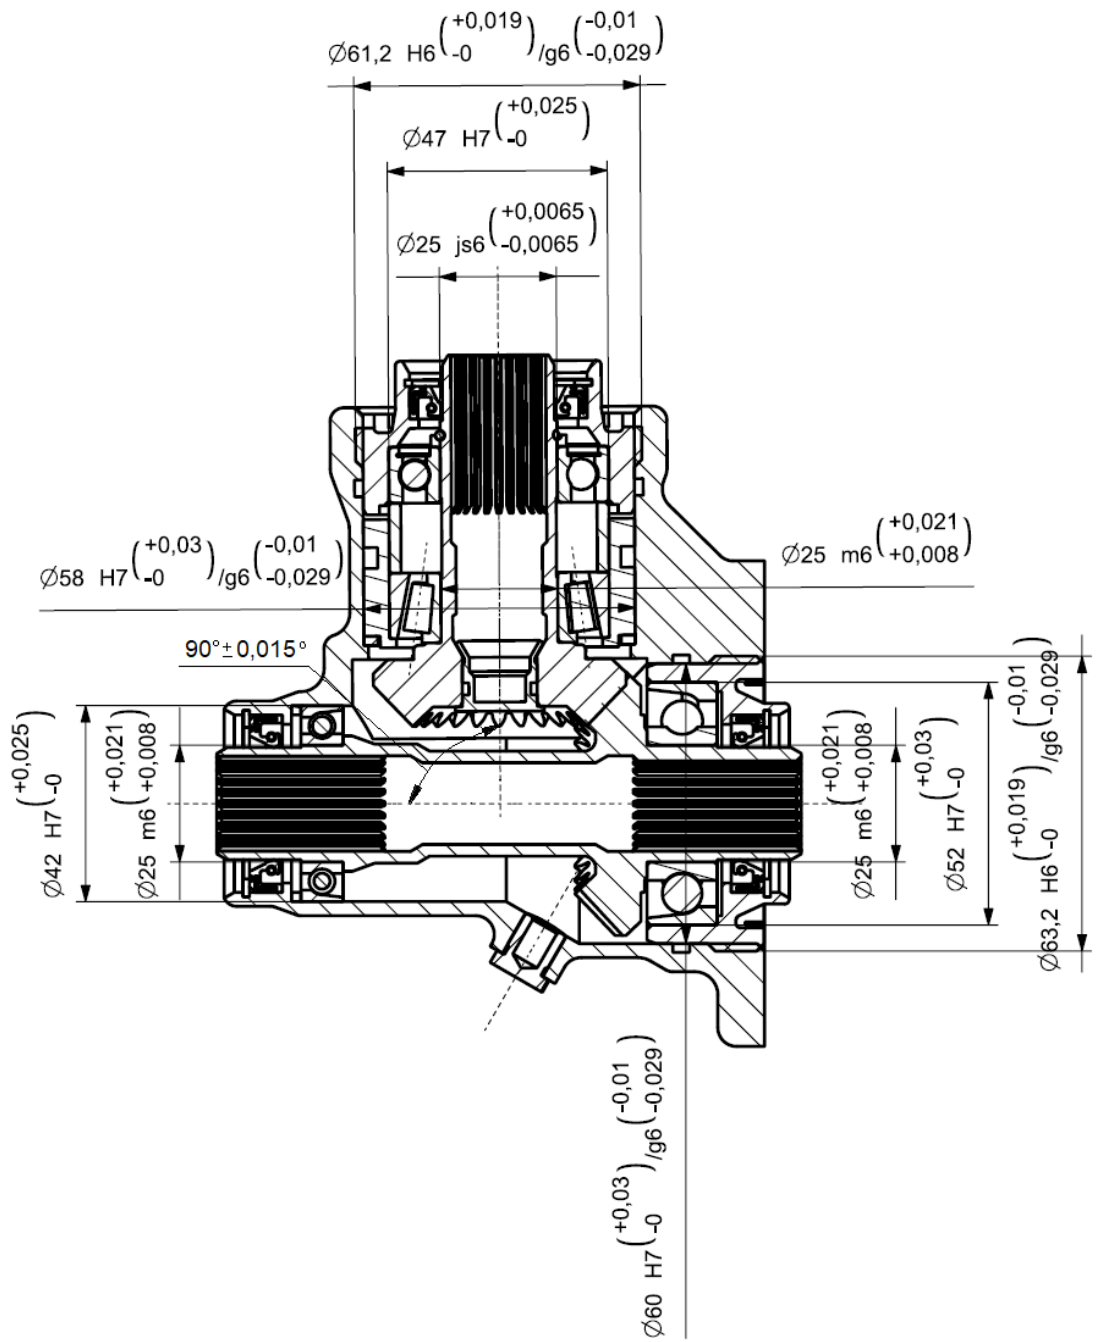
Допуски и посадки сборочных размеров
